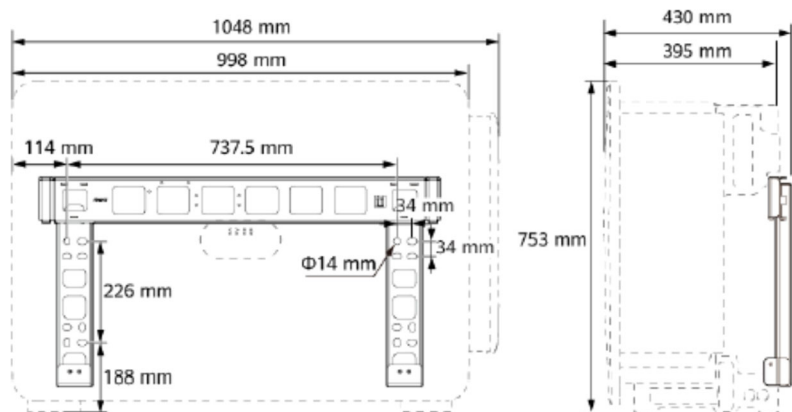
Dimensioni dell'inverter e staffa di fissaggio
